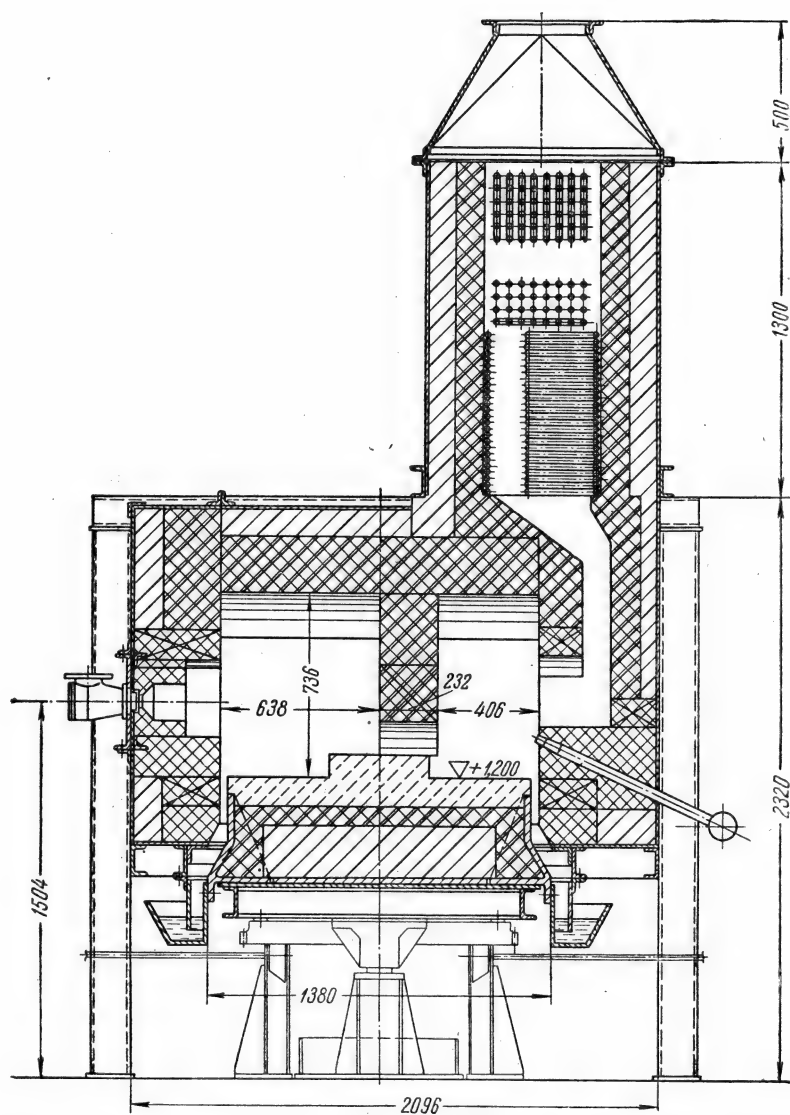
Переоборудование на газ камерной нагревательной печи с вращающимся подом для безокислительного нагрева металла.
